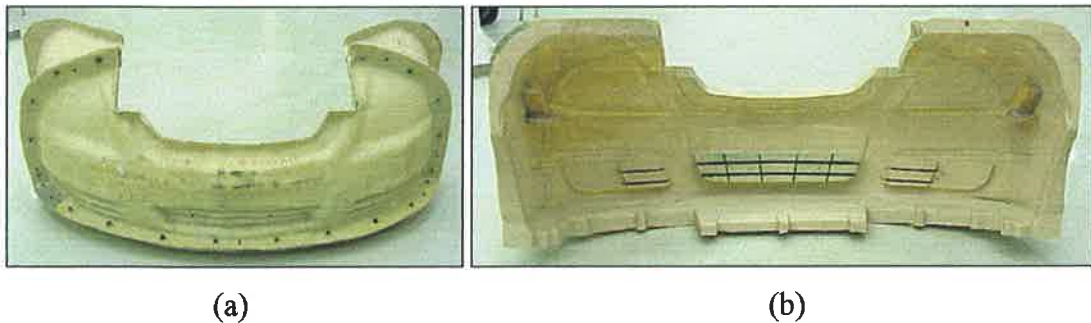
(a) Vista externa de molde laminado em 4 partes da frente parcial de um veículo; (b) Vista interna do mesmo molde. (Macarrão, 2004).
